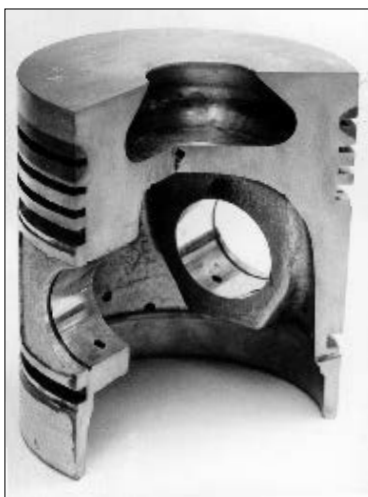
Внешний вид поршня после наплавки и проточки канавки в зоне сопряжения с первым компрессионным кольцом
